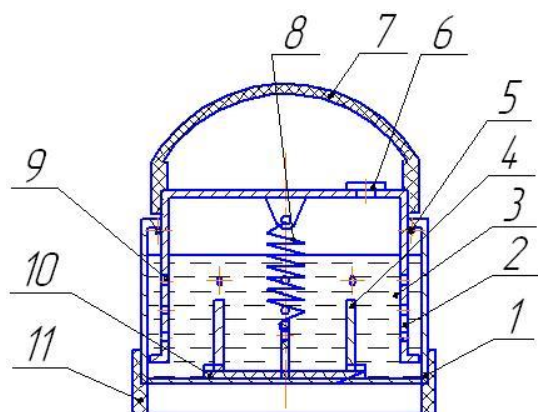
Металлический огнетушитель парового типа: 1 – резервуар; 2 – корпус; 3 – вода; 4 – нагревательное устройство; 5 – уплотнитель; 6 – пробка; 7 – амортизатор; 8 – пружина; 9 – отверстия для вывода пара; 10 – изолятор; 11 – эластичная
